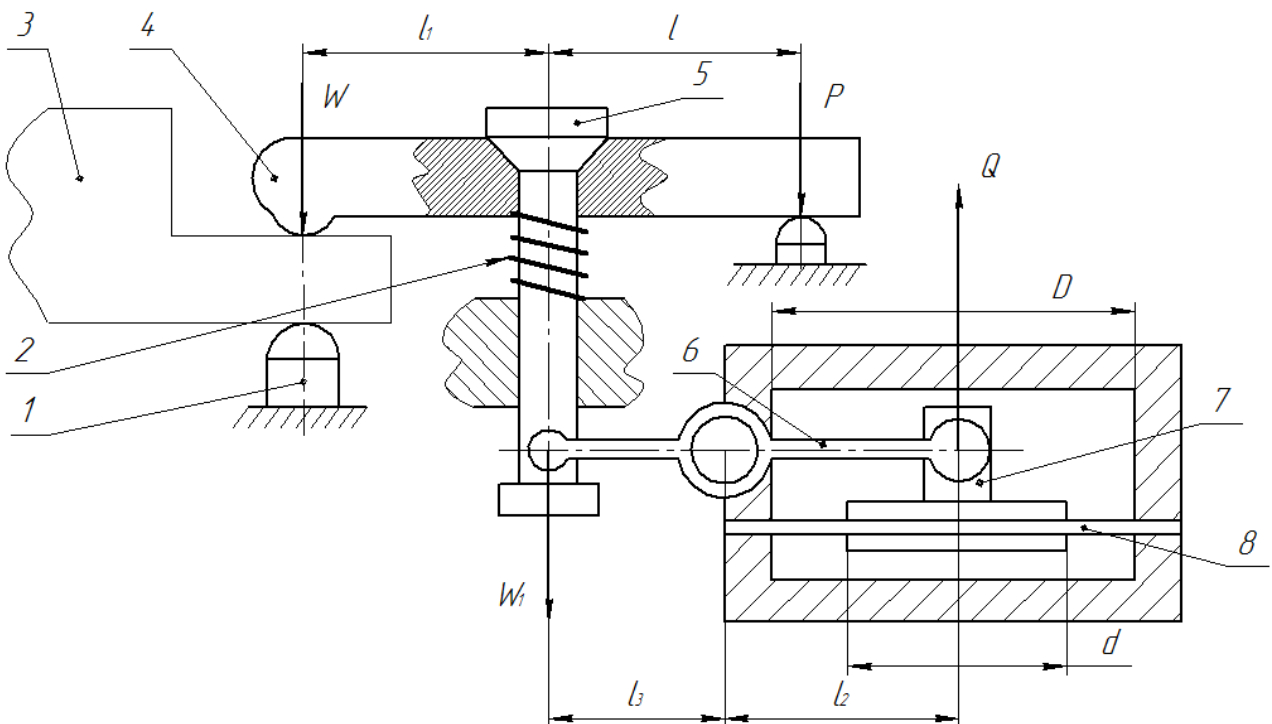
Схема й параметри комбінованого затискного пристрою із пневмоприводом: 1 – опора; 2 – пружина; 3 – деталь; 4 – планка; 5 – стрижень; 6 – важіль-підсилювач; 7 – шток мембрани; 8 – мембрана; W , W_1 – сила затискача; Q – сила на штоку пневмокамери; P – реакція опори; l , l_1 , l_2 , l_3 – довжини плечей важелів
